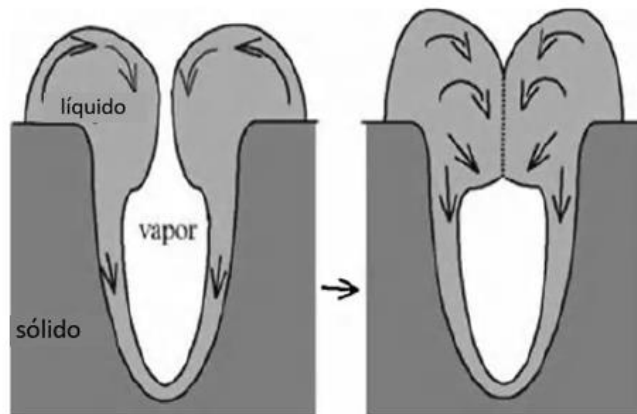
Esquema de la formación de grandes poros debido al llenado completo del hueco clave durante la soldadura láser[2].
